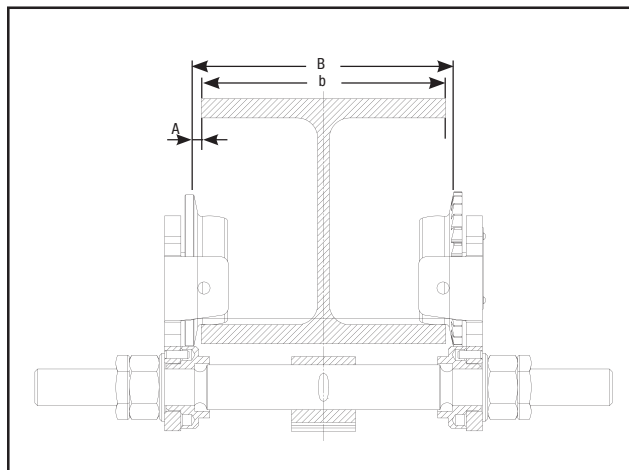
Chariot installé sur la poutrelle I-Beam.
